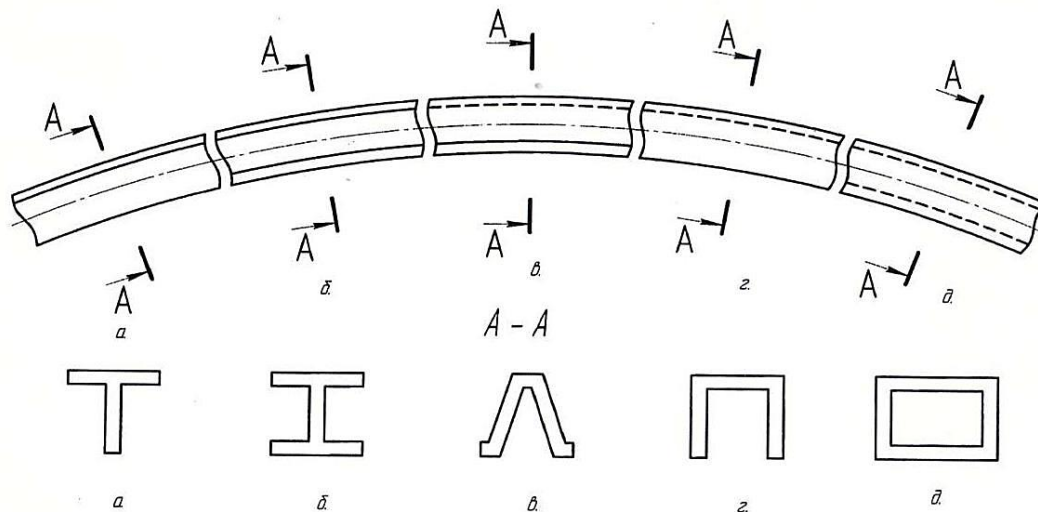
Поперечні перетини деталей із профілів, виготовлених способом пластичного гнуття
